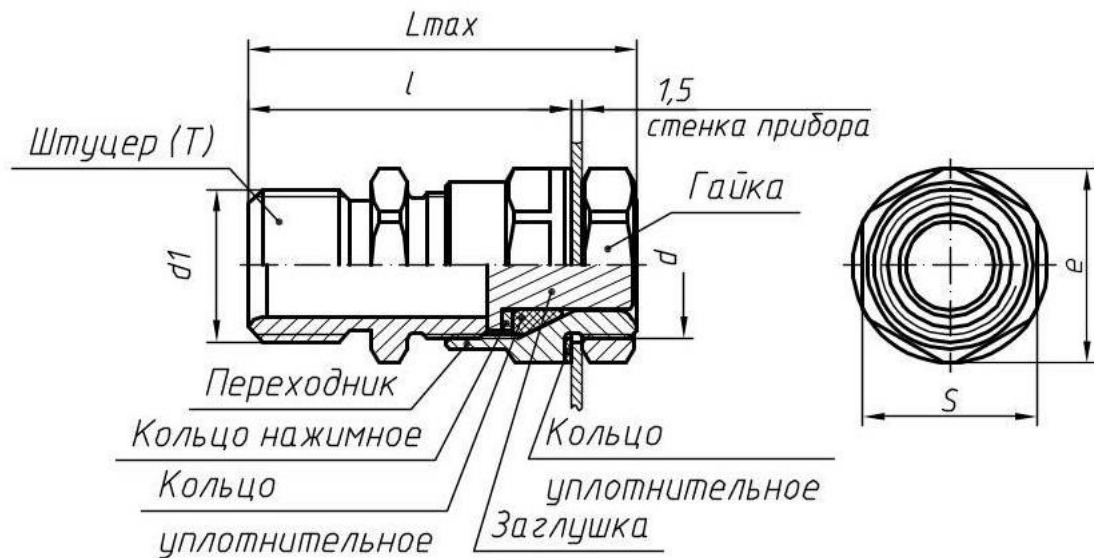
ЕхеКВУ-Т – для прокладки кабеля в трубе (остальное см. рис.Б.1)
